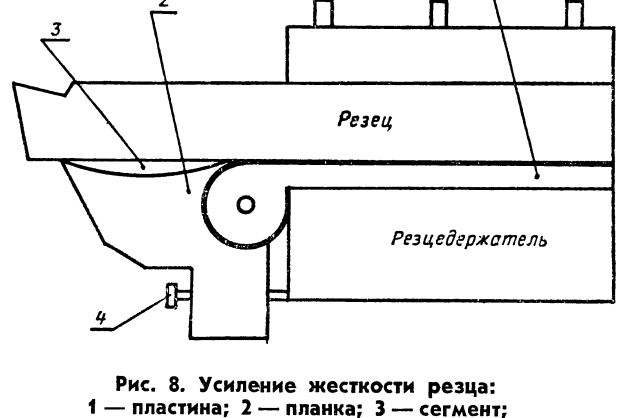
Усиление жесткости резца: 1 — пластина; 2 — планка; 3 — сегмент; 4 — винт регулировочный
